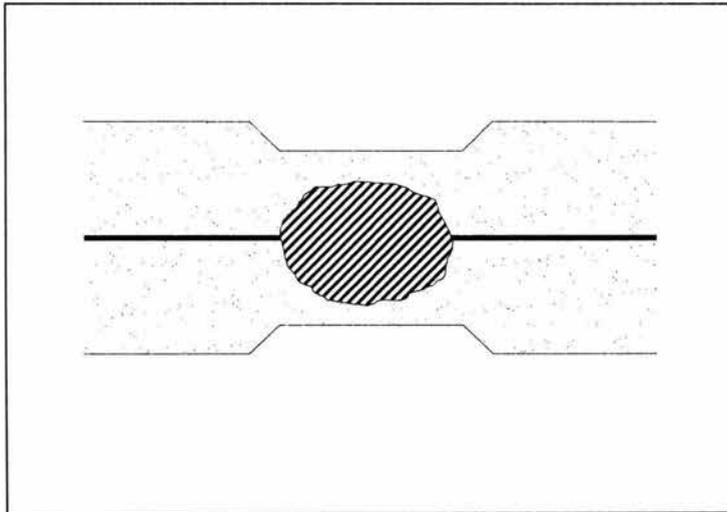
Soldadura incorrecta, por excesivo penetración de los electrodos.
